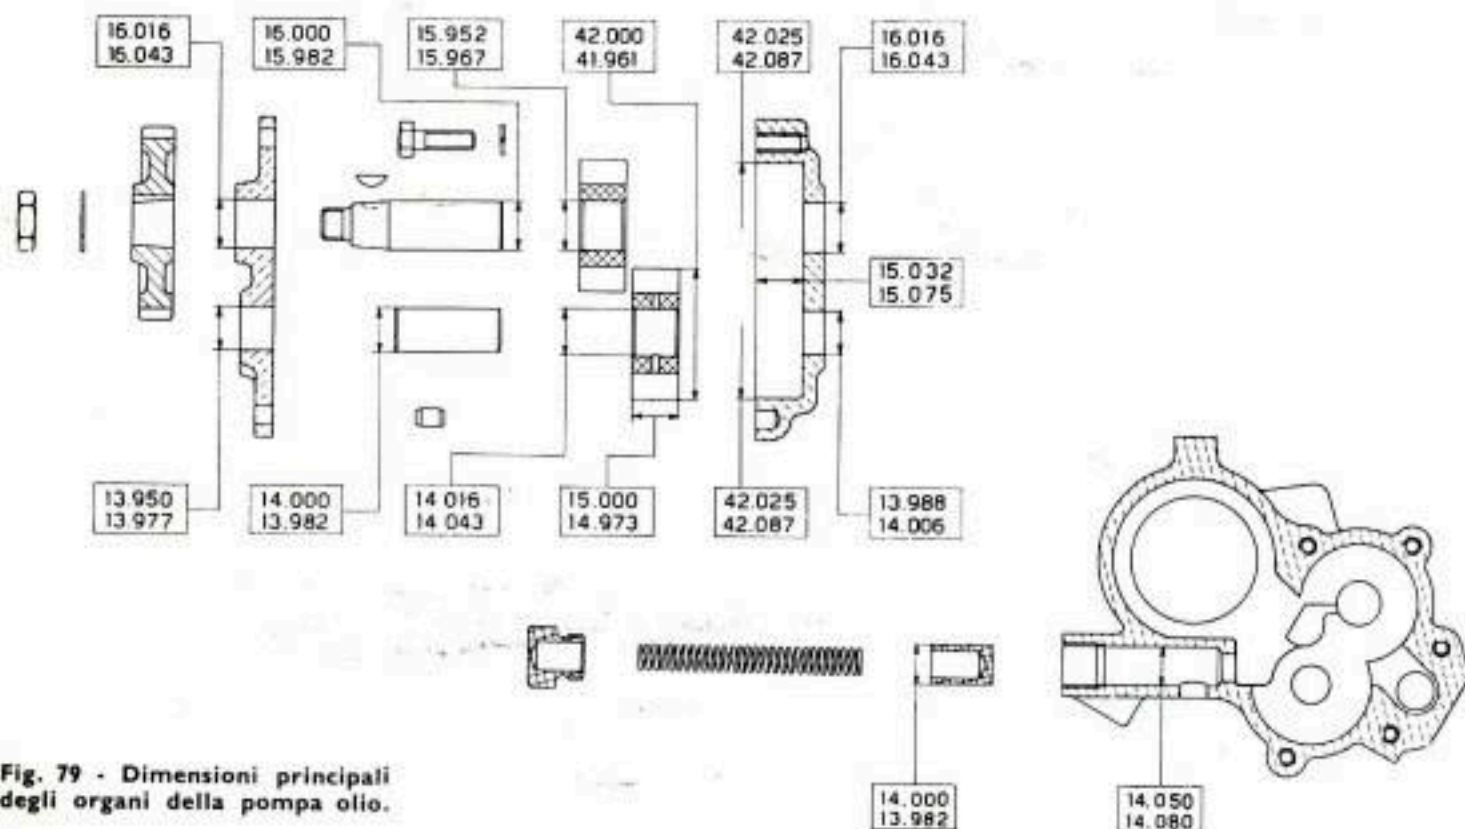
Dimensioni principali degli organi della pompa olio.
